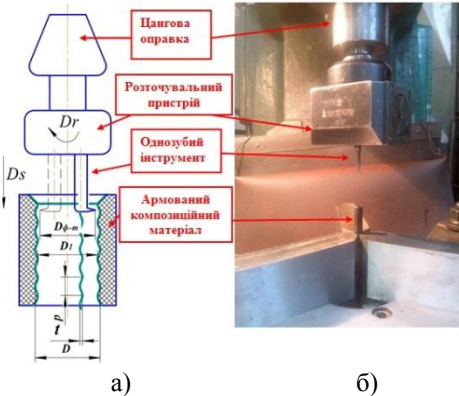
Обробка круглої різьби в АКМ: а – спрощена схема обробки; б – фото процесу обробки.
